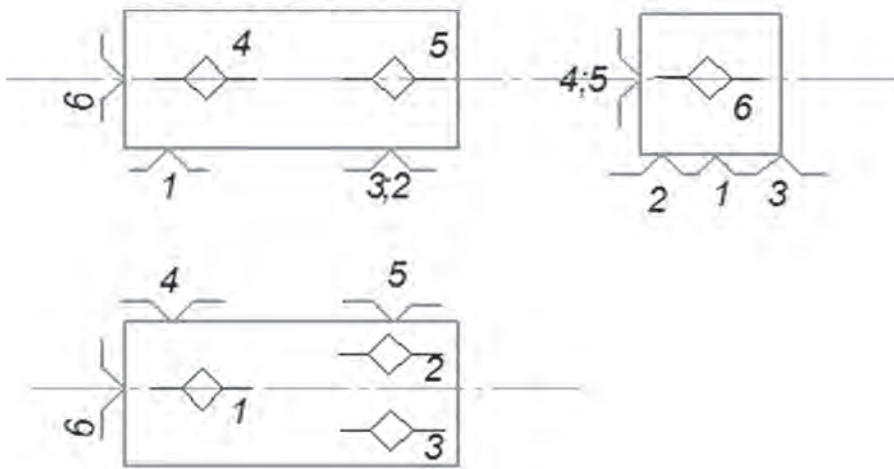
Встановлення заготовки на шести опорних точках: 1...6 – опорні точки
